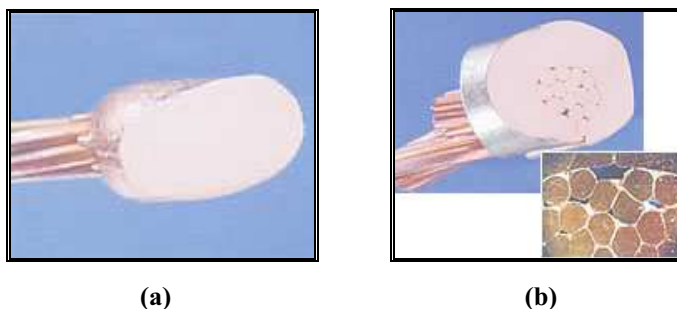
(a) Conexão por solda. (b) Conexão mecânica.
